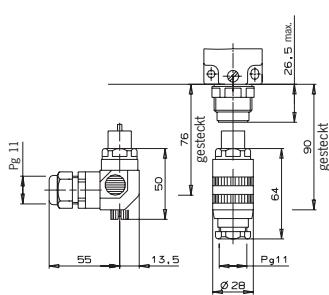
Maßzeichnung NZ2VZ-5... mit Steckverbinder SR6
